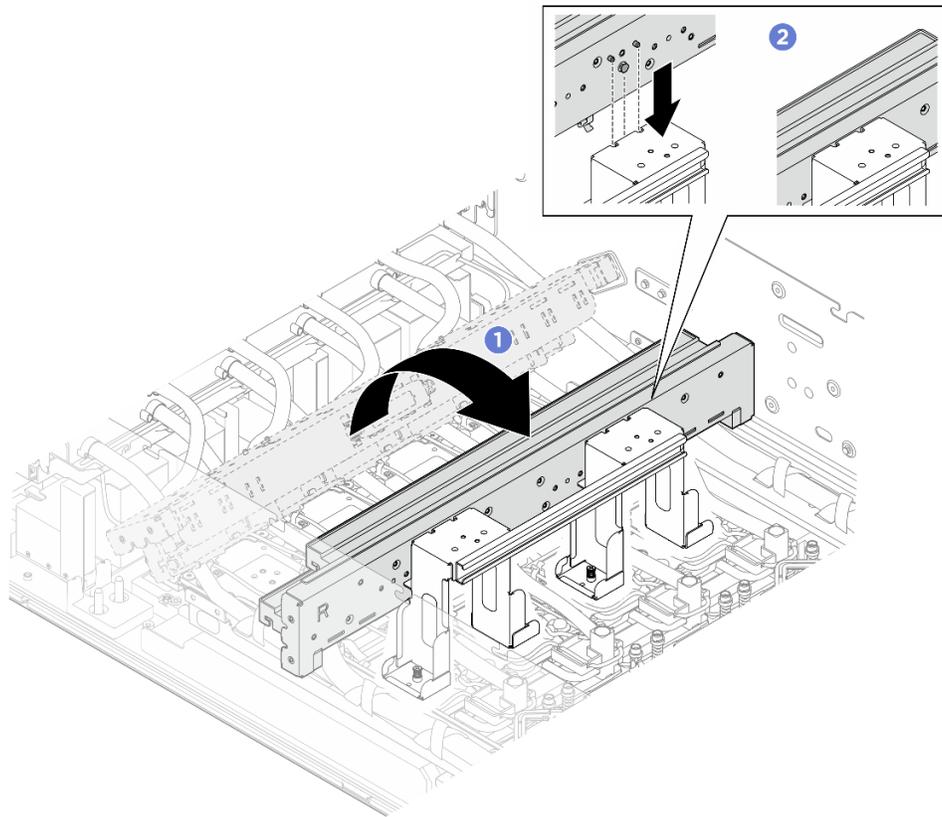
Repositionnement du collecteur du module de plaque froide GPU arrière
